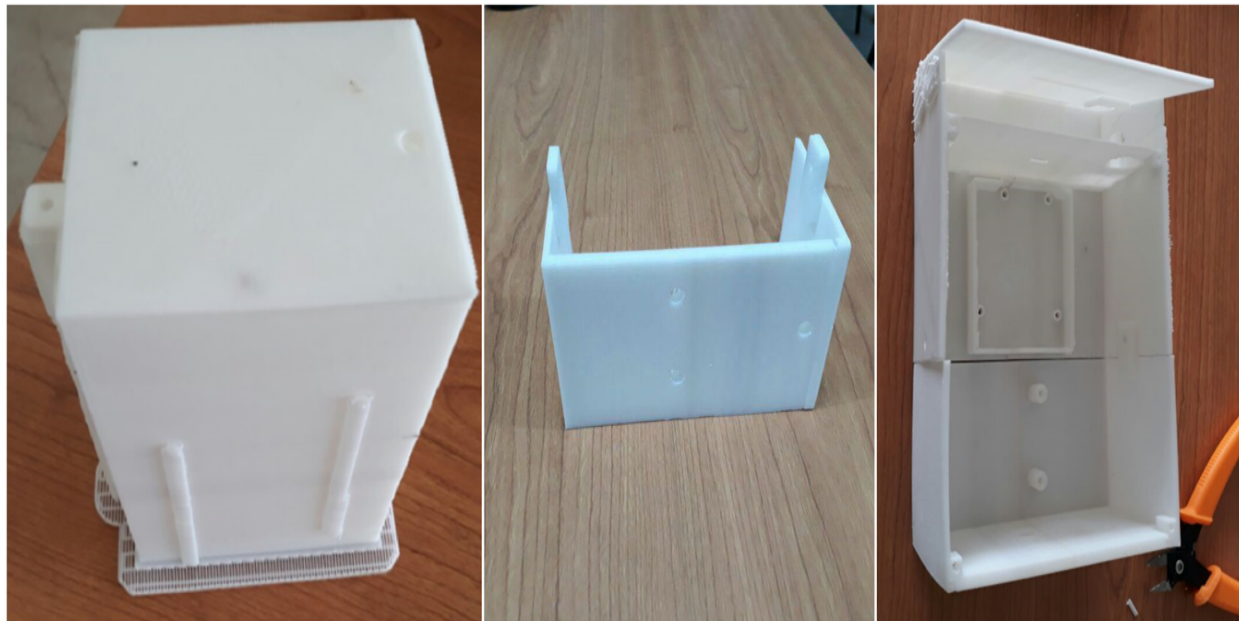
Piezas impresas en 3D para la estructura de la caja. *Fuente: Autor.
